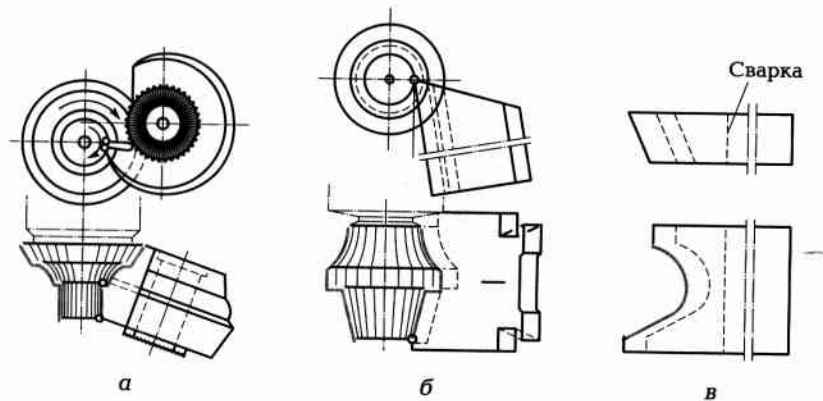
Обработка дисковыми (а), призматическими (б) и стержневыми (в) фасонными резцами
